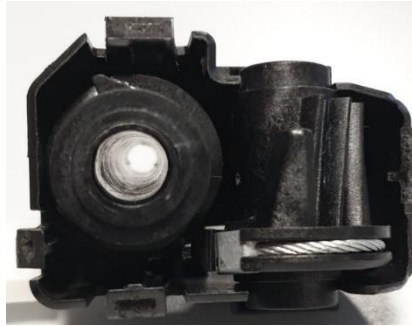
Sistema de engrenagens com cabo de aço enrolado
